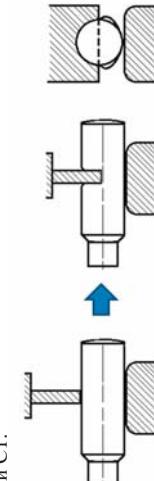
Схема процесу вдавлювання вулькового бойка в заготовку
